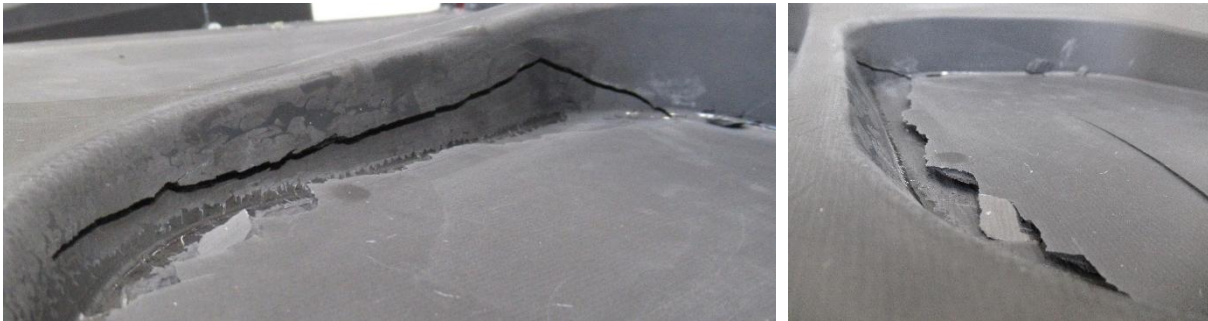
Detailaufnahme der Beschädigung des Werkzeuges.
